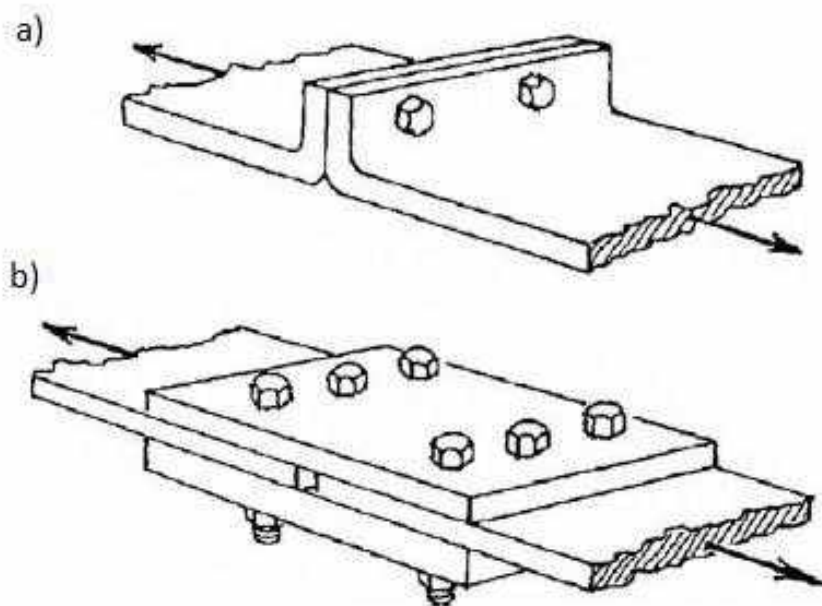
a) junta de tração. b) junta de cisalhamento (BICKFORD, 2008)
